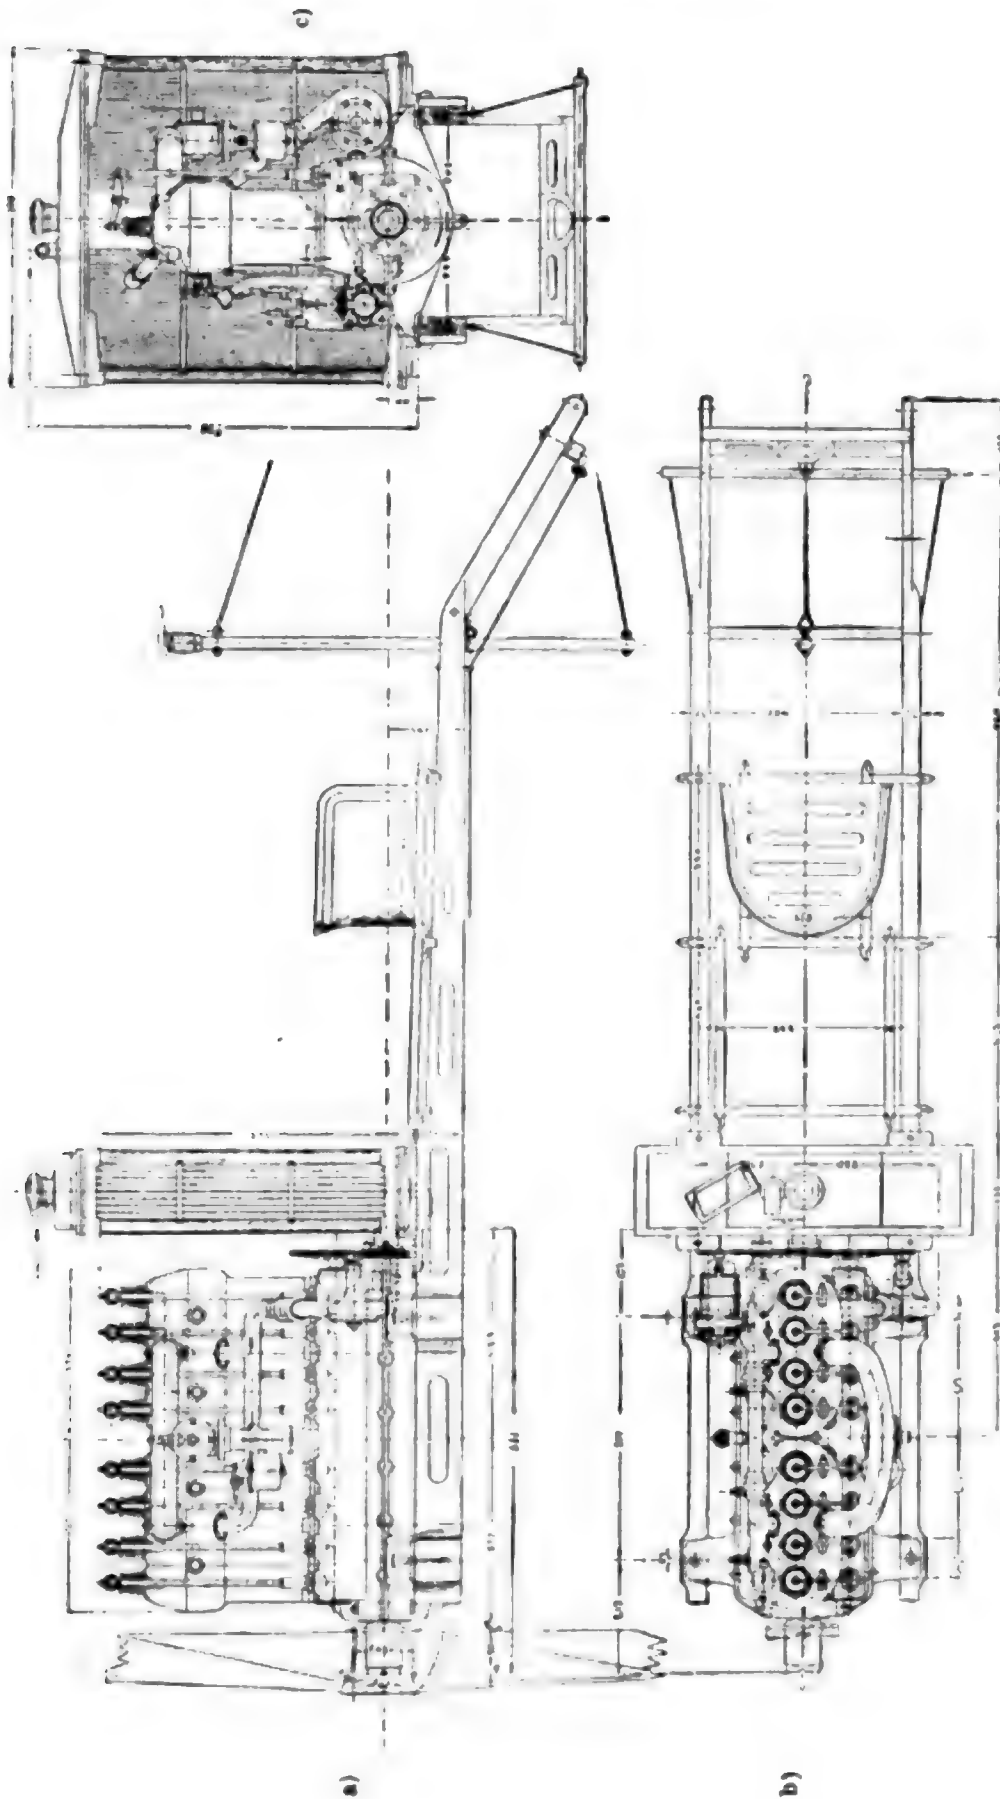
Einbau des „Argus“-Flugmotors. Fig.: a) Seitenansicht, b) Draufsicht, c) Vorderansicht.
